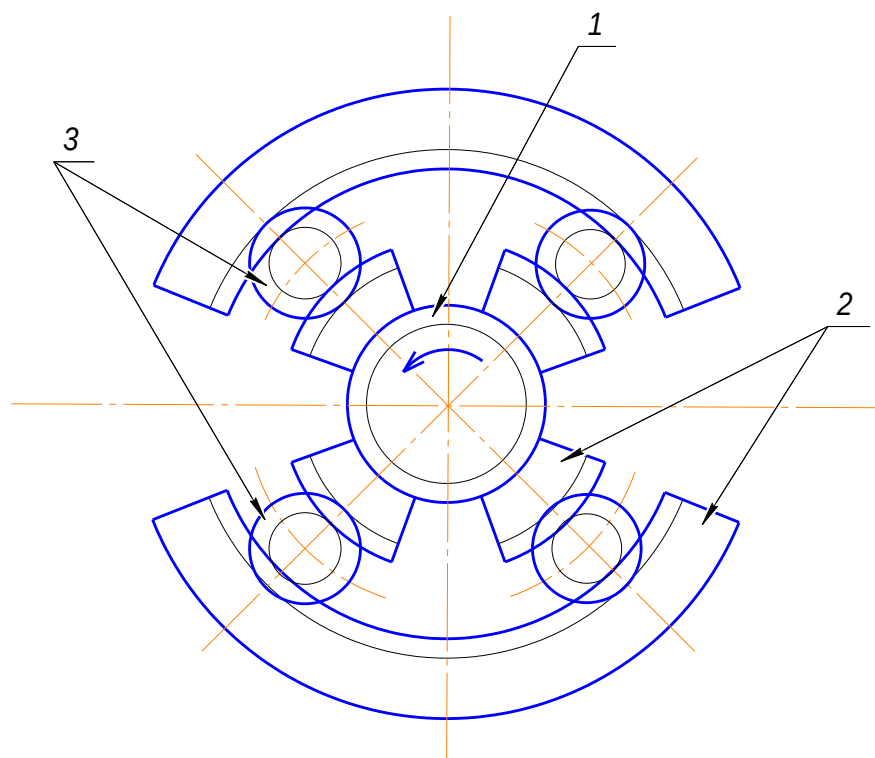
б – Планетарный процесс накатывания: 1 – вращающийся резьбовой ролик; 2 – подвижные сегменты; 3 – обрабатываемые детали
